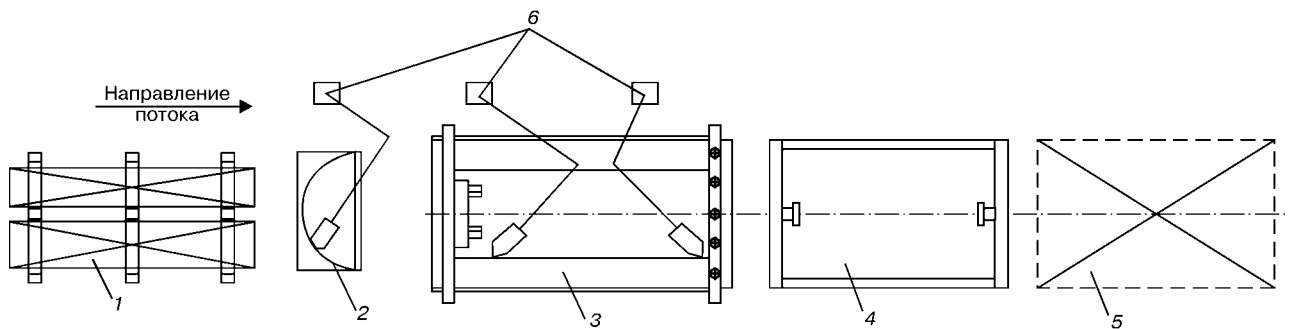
Схема размещения оборудования на линии изготовления крыш: 1 — складское место для листового проката; 2 — стенд сборки и сварки фрамуг; 3 — установка сборки и сварки; 4 — стенд испытания сварных соединений на плотность; 5 — складское место готовых изделий; 6 — двухплечевые консоли с подающими механизмами сварочных полуавтоматов
